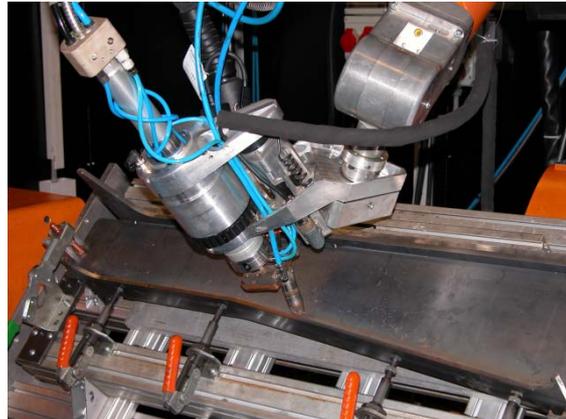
MSG-Laserstrahlhybridschweißen trägerförmiger Schienenfahrzeugkomponenten
